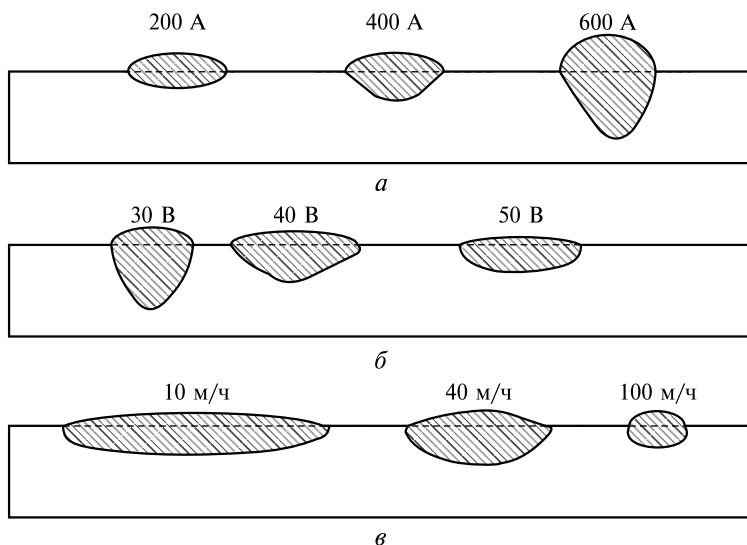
Влияние параметров режима сварки на форму шва:
